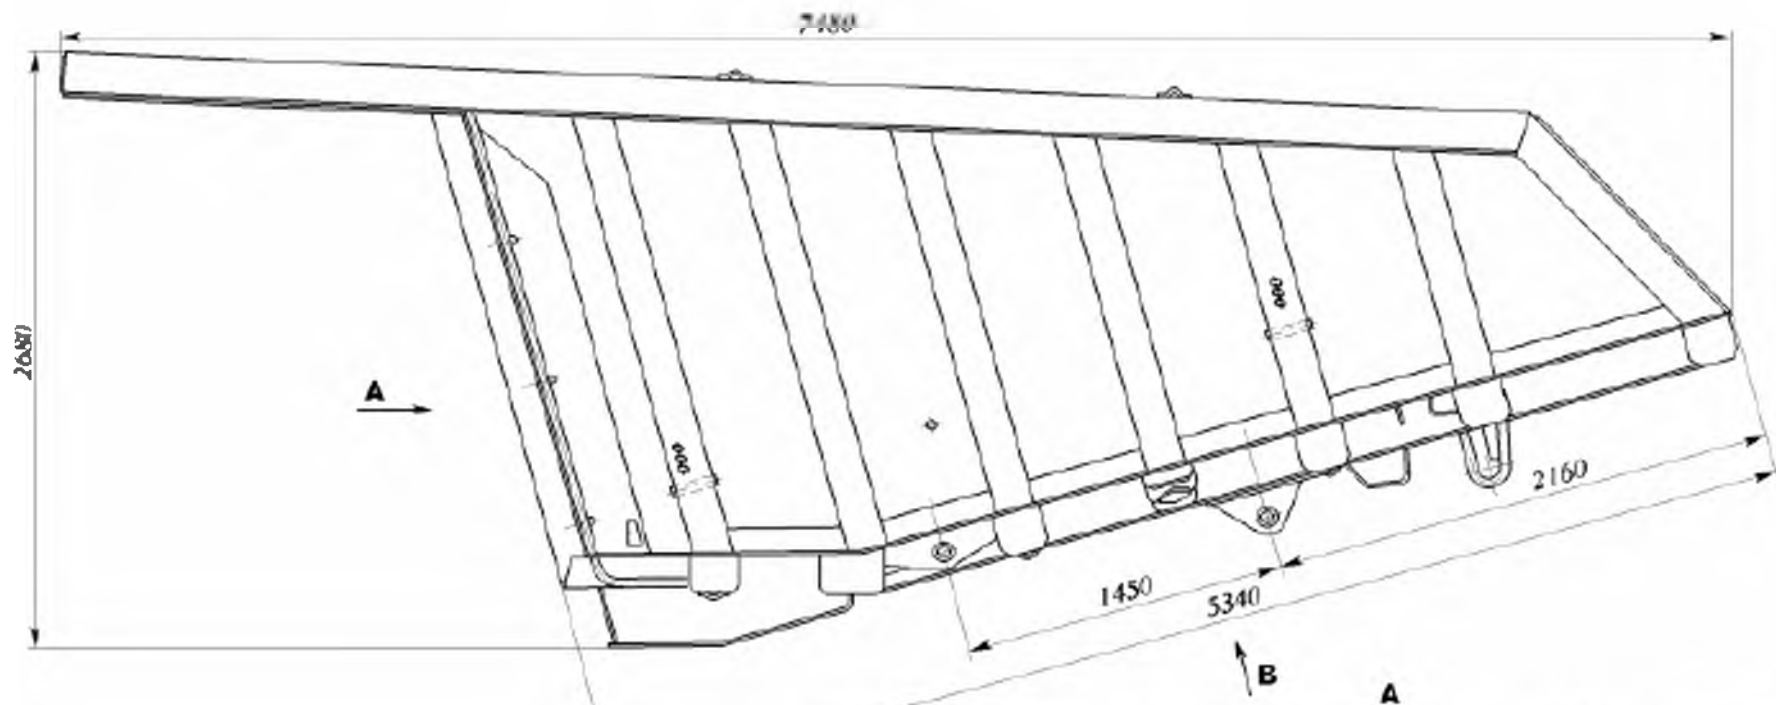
Сборка и сварка платформы самосвала-углевоза БелАЗ-75479 (Вид В показан на рисунке 19.11)
